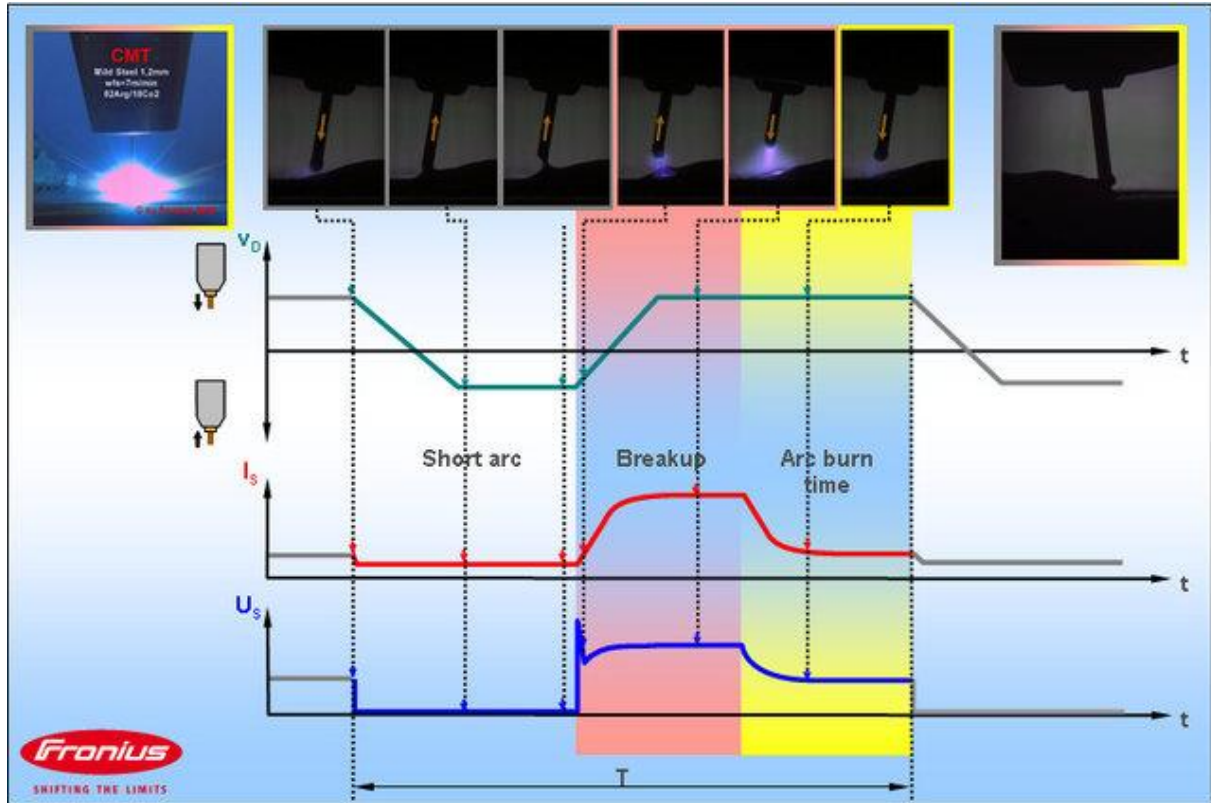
Принципова схема процесу холодного зварювання
